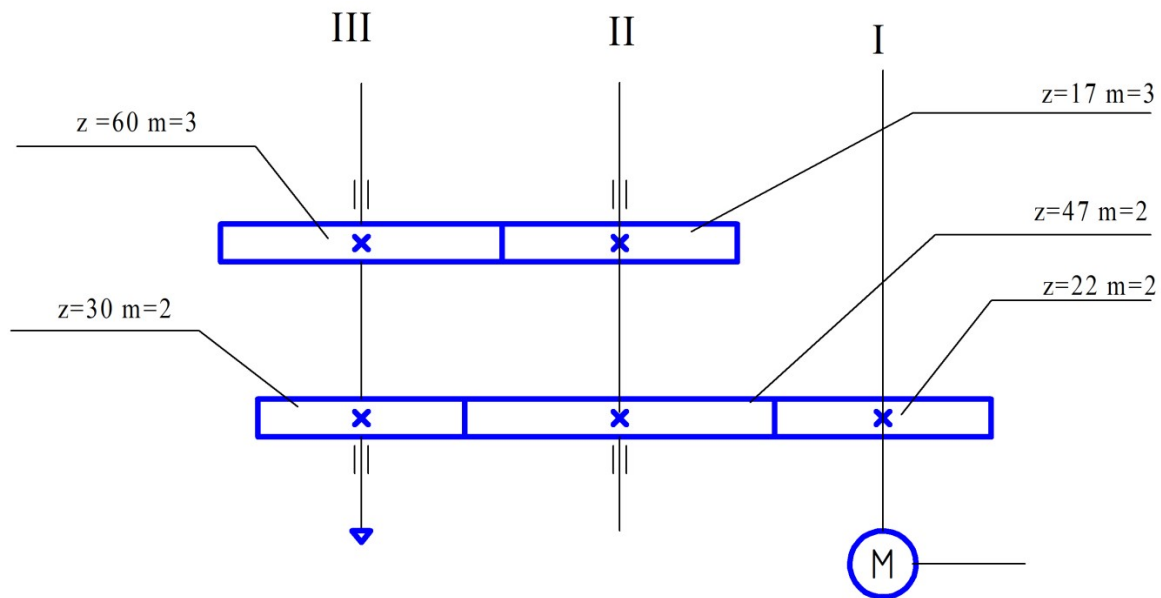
Кінематична схема приводу шпинделя координатно-свердильного верстата
